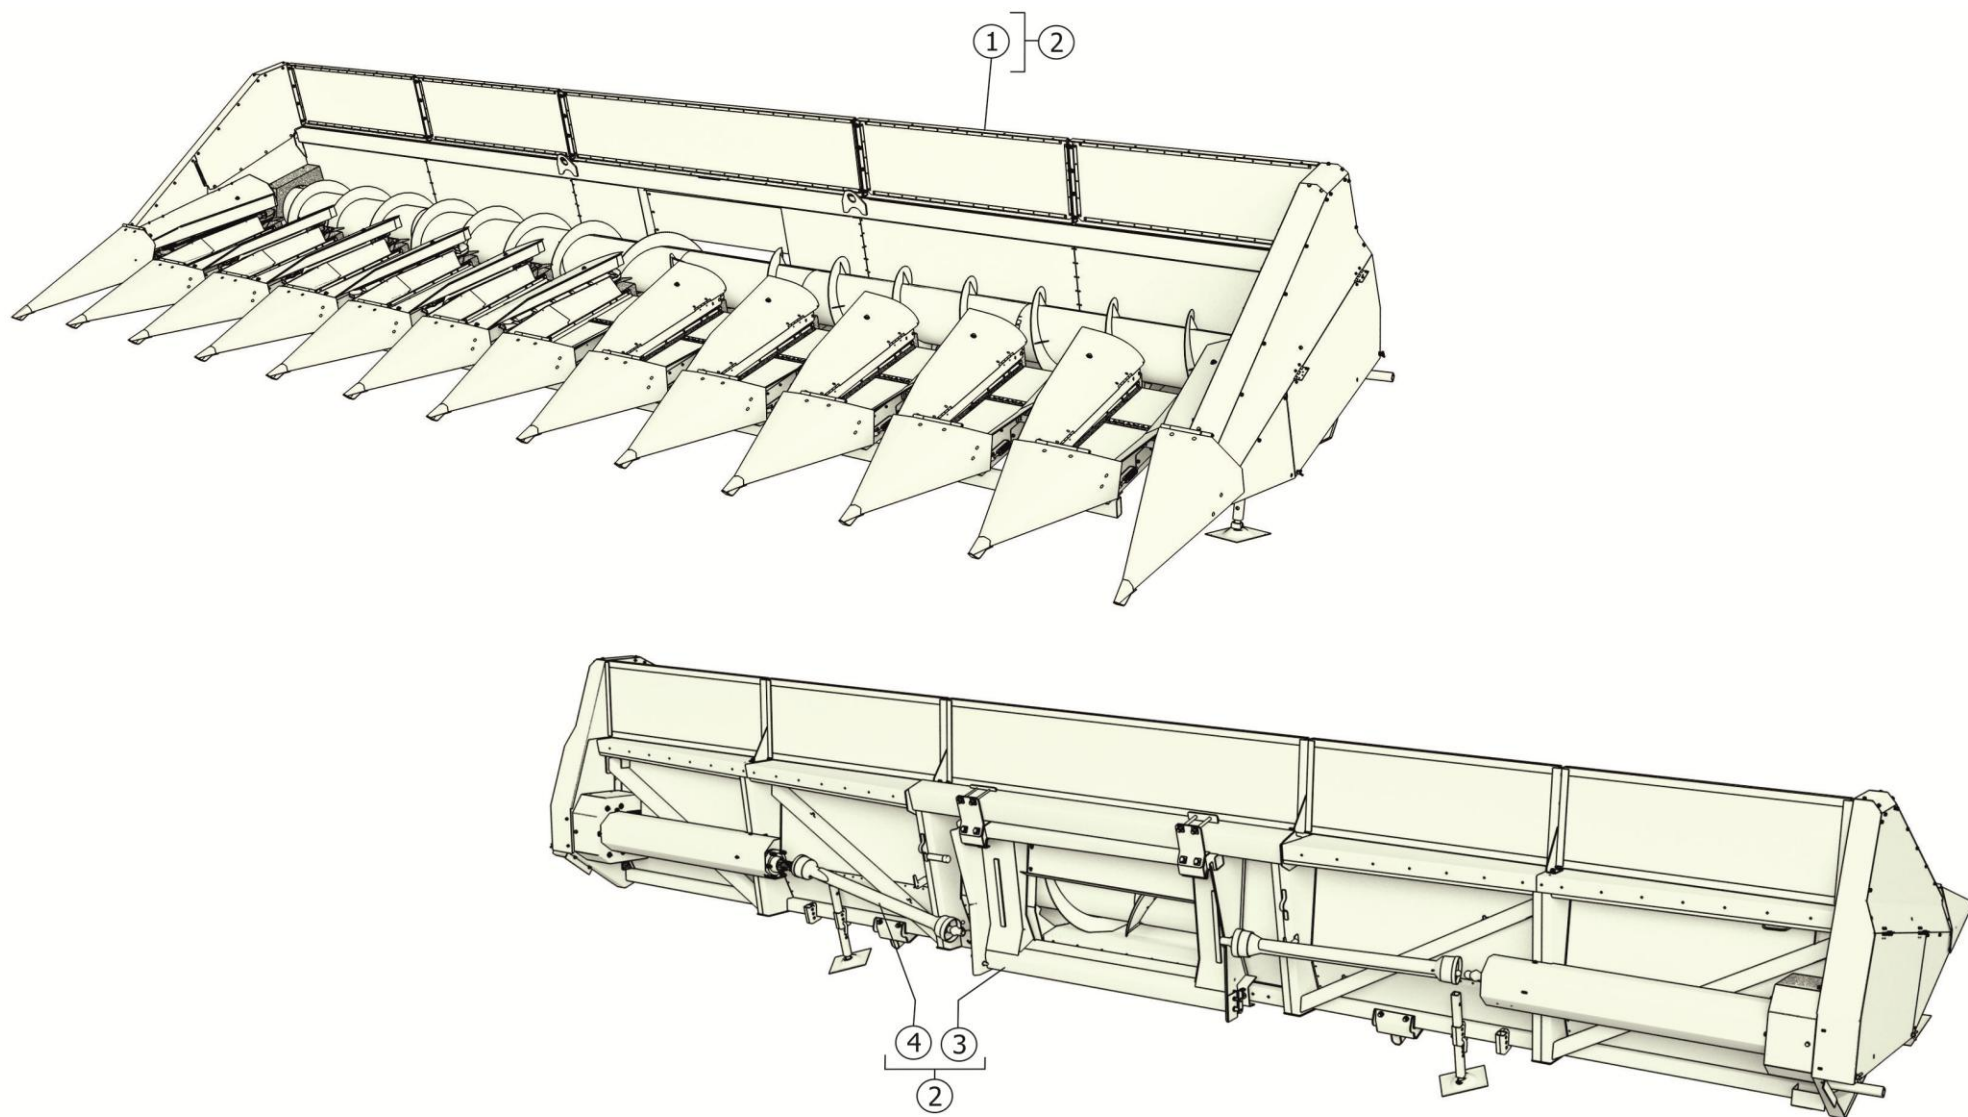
Приспособление для уборки подсолнечника ПСП-1270-05
